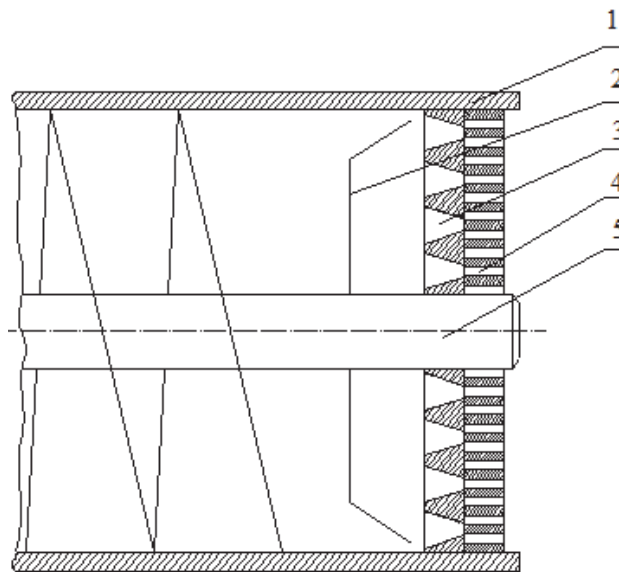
Узел измельчения: 1 – корпус; 2 – крестовидный нож; 3 – стационарно установленный нож-решетка; 4 – вращающийся нож-решетка; 5 – вал узла измельчения
